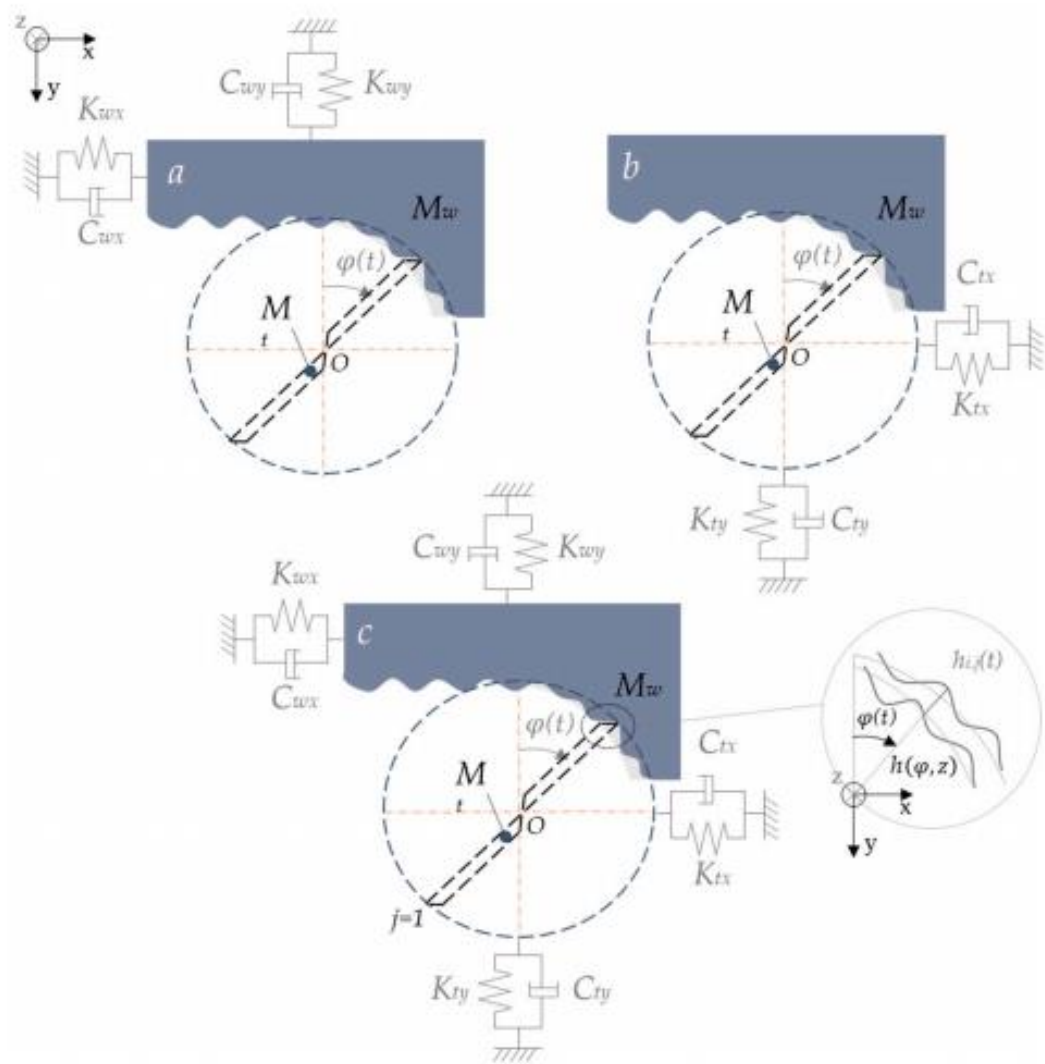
Можливі моделі динаміки фрезерування тонкостінних елементів заготовок [12]
